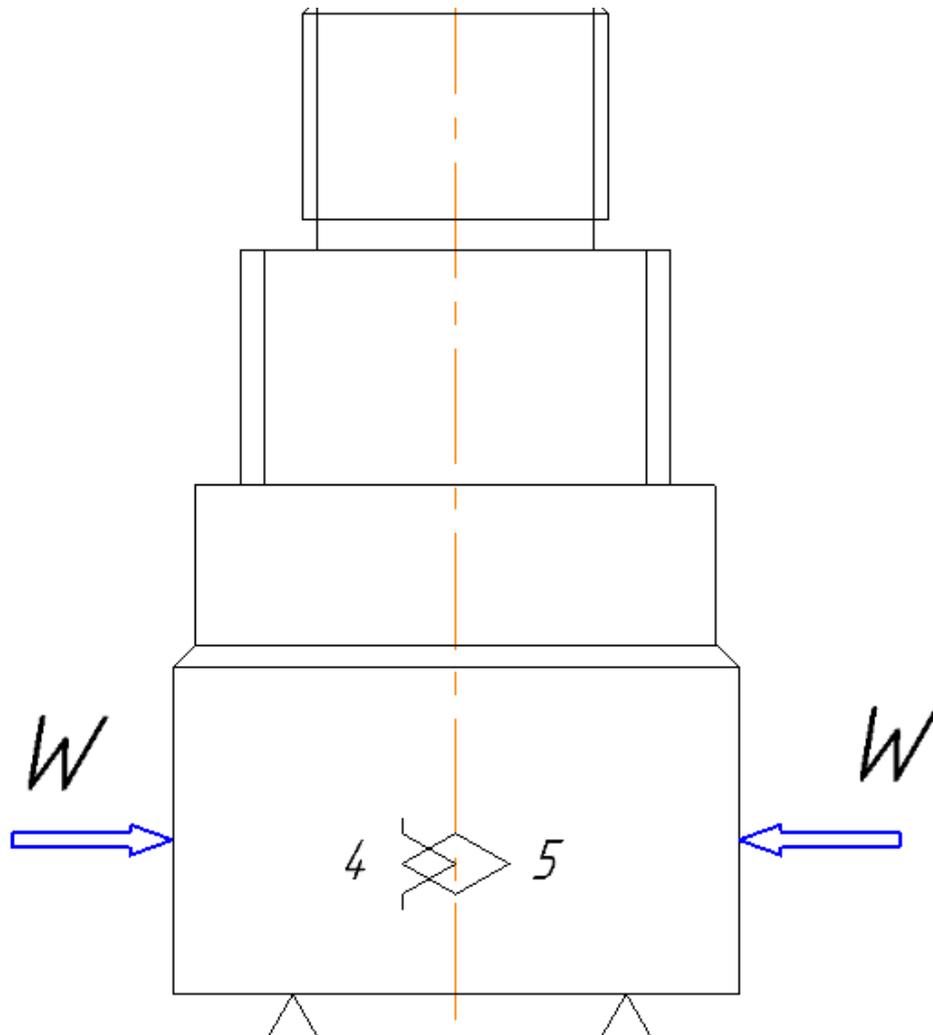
Принципиальная схема зажима заготовки в приспособлении с указанием мест приложения силы зажима.
